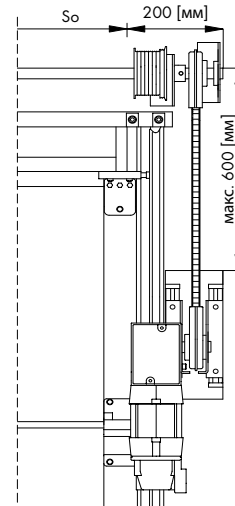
Передача переносящая привод – нестандартная версия (установка перед направляющей).
